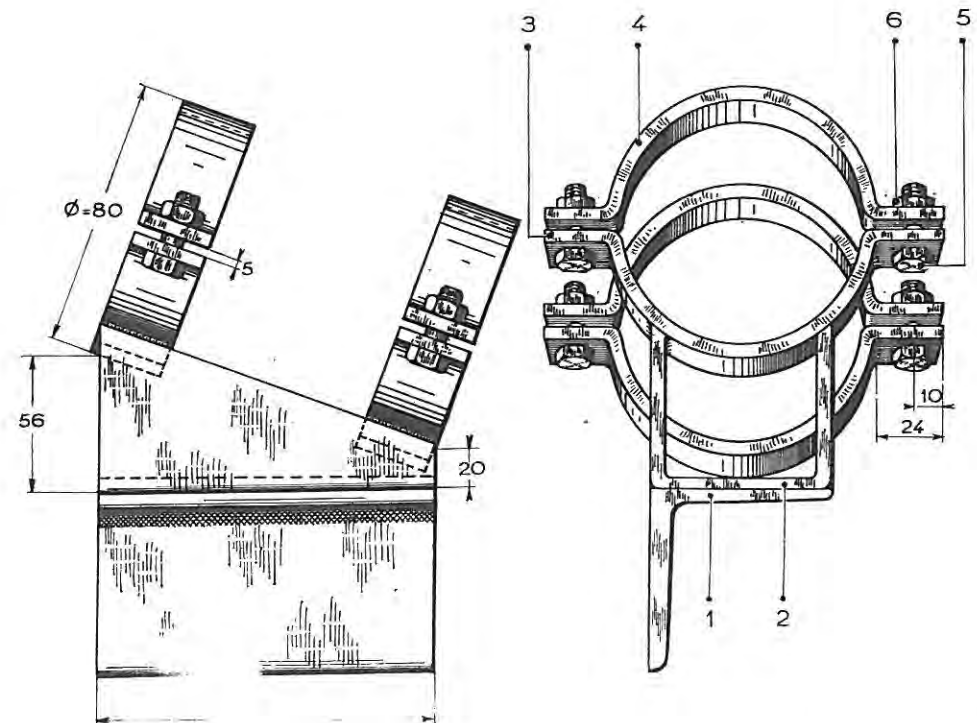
Stütze für Halterung der hinteren Achse im Schraubstock MR-3053-90
